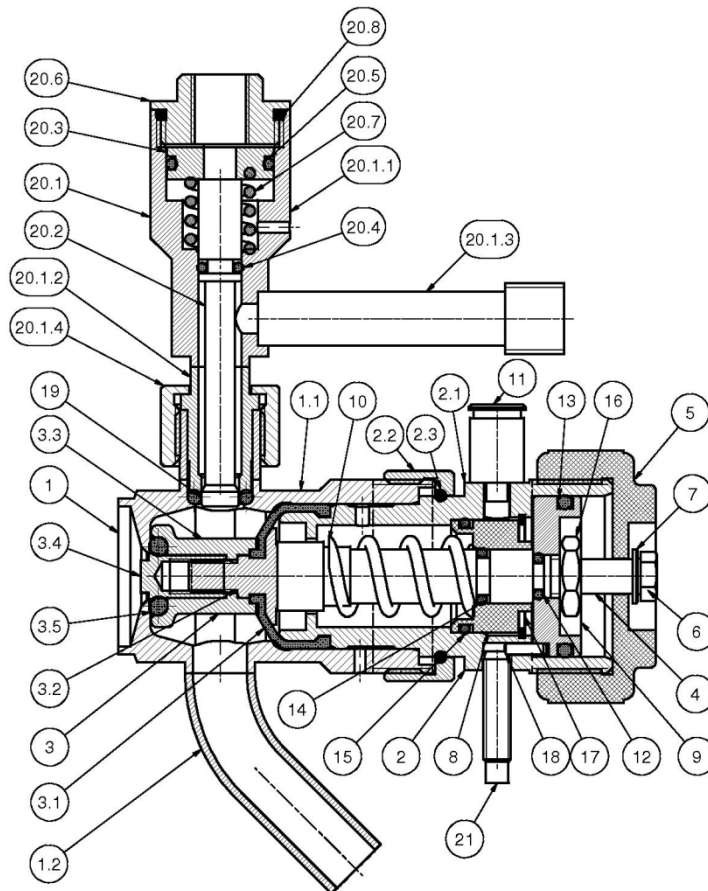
Schnitt PharmCom–Probenahmeventil manuell / pneumatisch mit Spülventil und Nahrungsmittelinitiator
